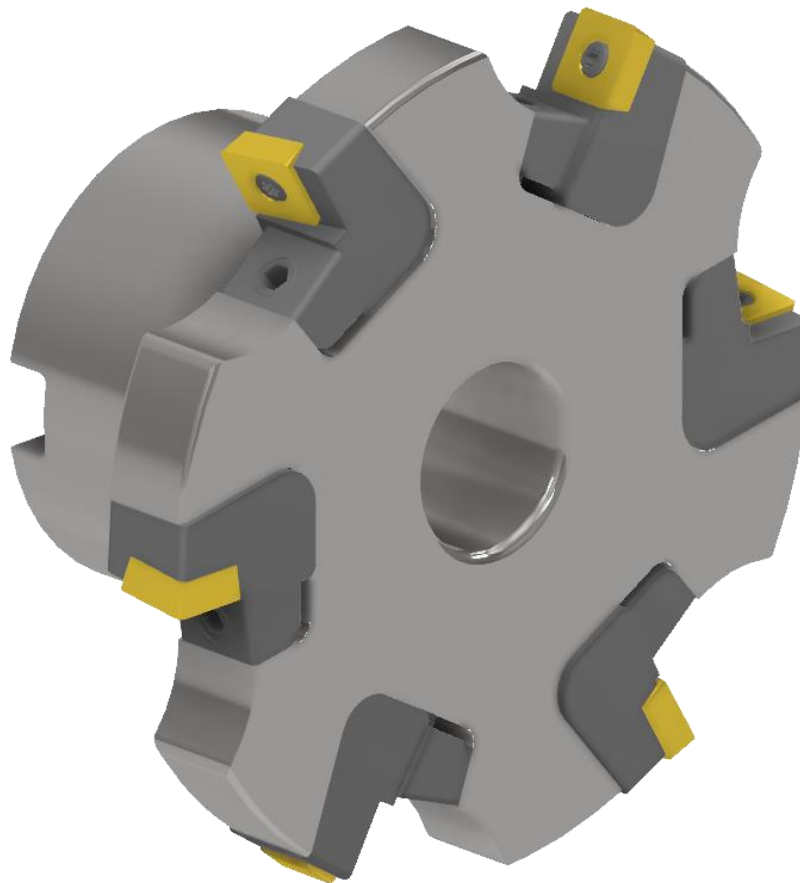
Збірної конструкція тристоронньої дискової фрези
